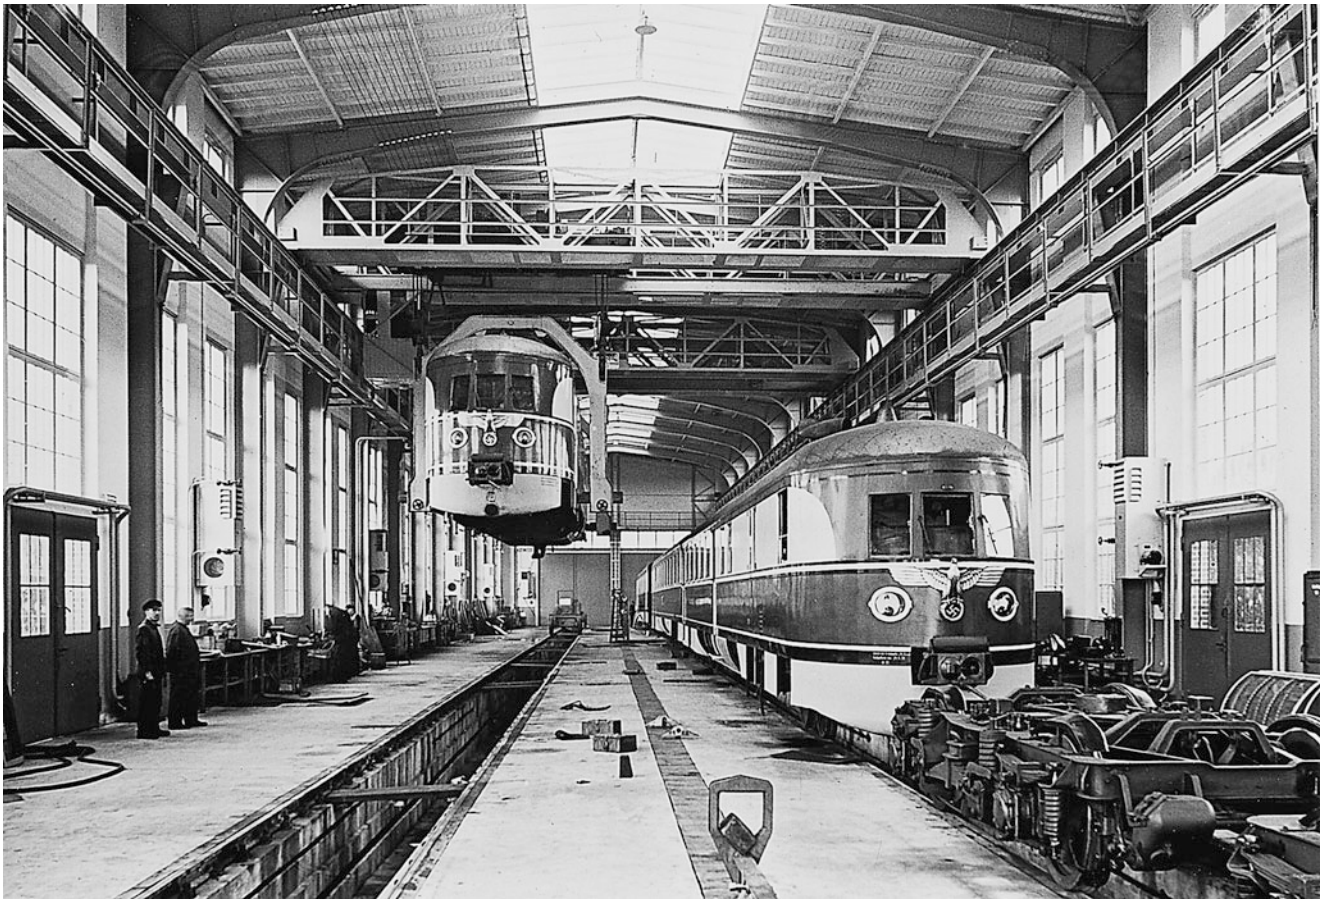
Das moderne Reichsbahn-Ausbesserungswerk für ihre Schnelltriebwagen befand sich in Wittenberge an der Strecke Berlin-Hamburg, hier mit Wagen der »Bauart Köln« in der Hebehalle
